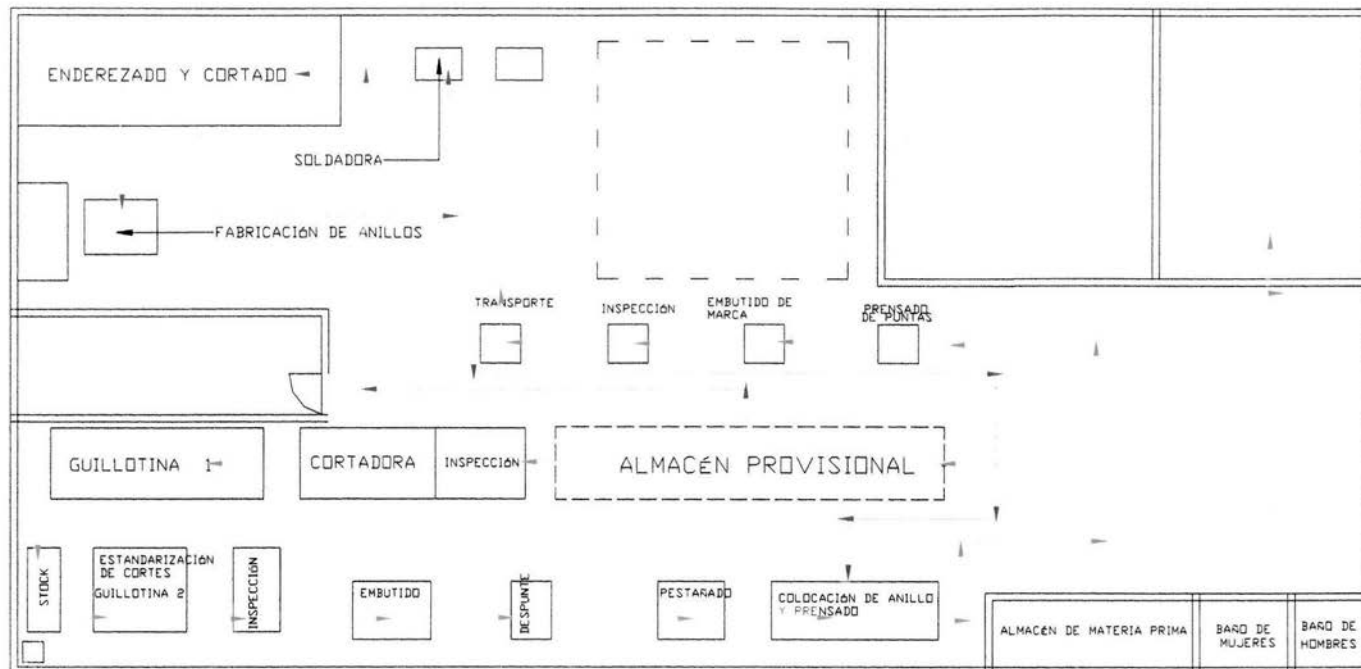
Distribución de planta de la empresa Lemus.
